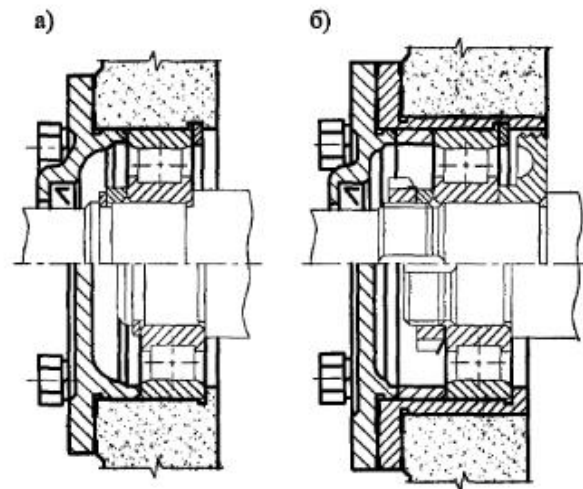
Установка наружного кольца разъемного подшипника в корпусе плавающей (самоустанавливающейся) опоры
